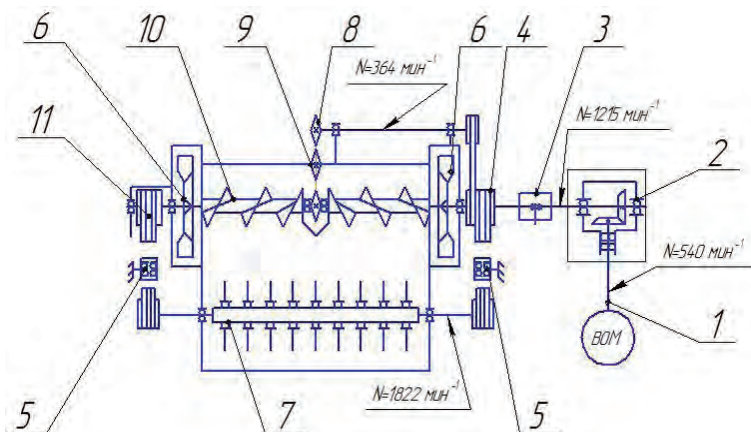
Роторный измельчитель соломы РИС – 2
